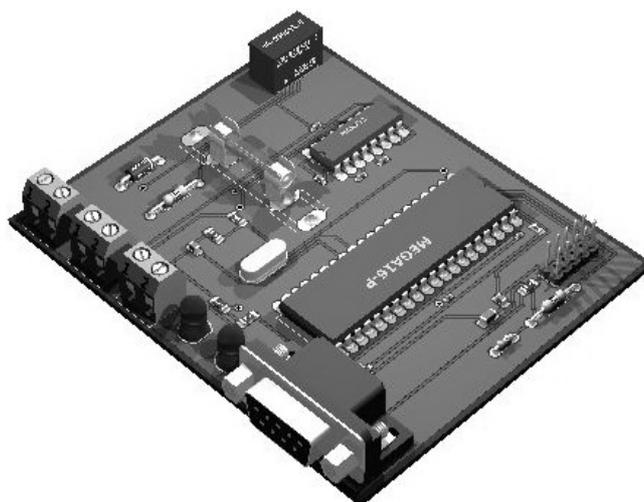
Трехмерный макет разрабатываемого устройства
